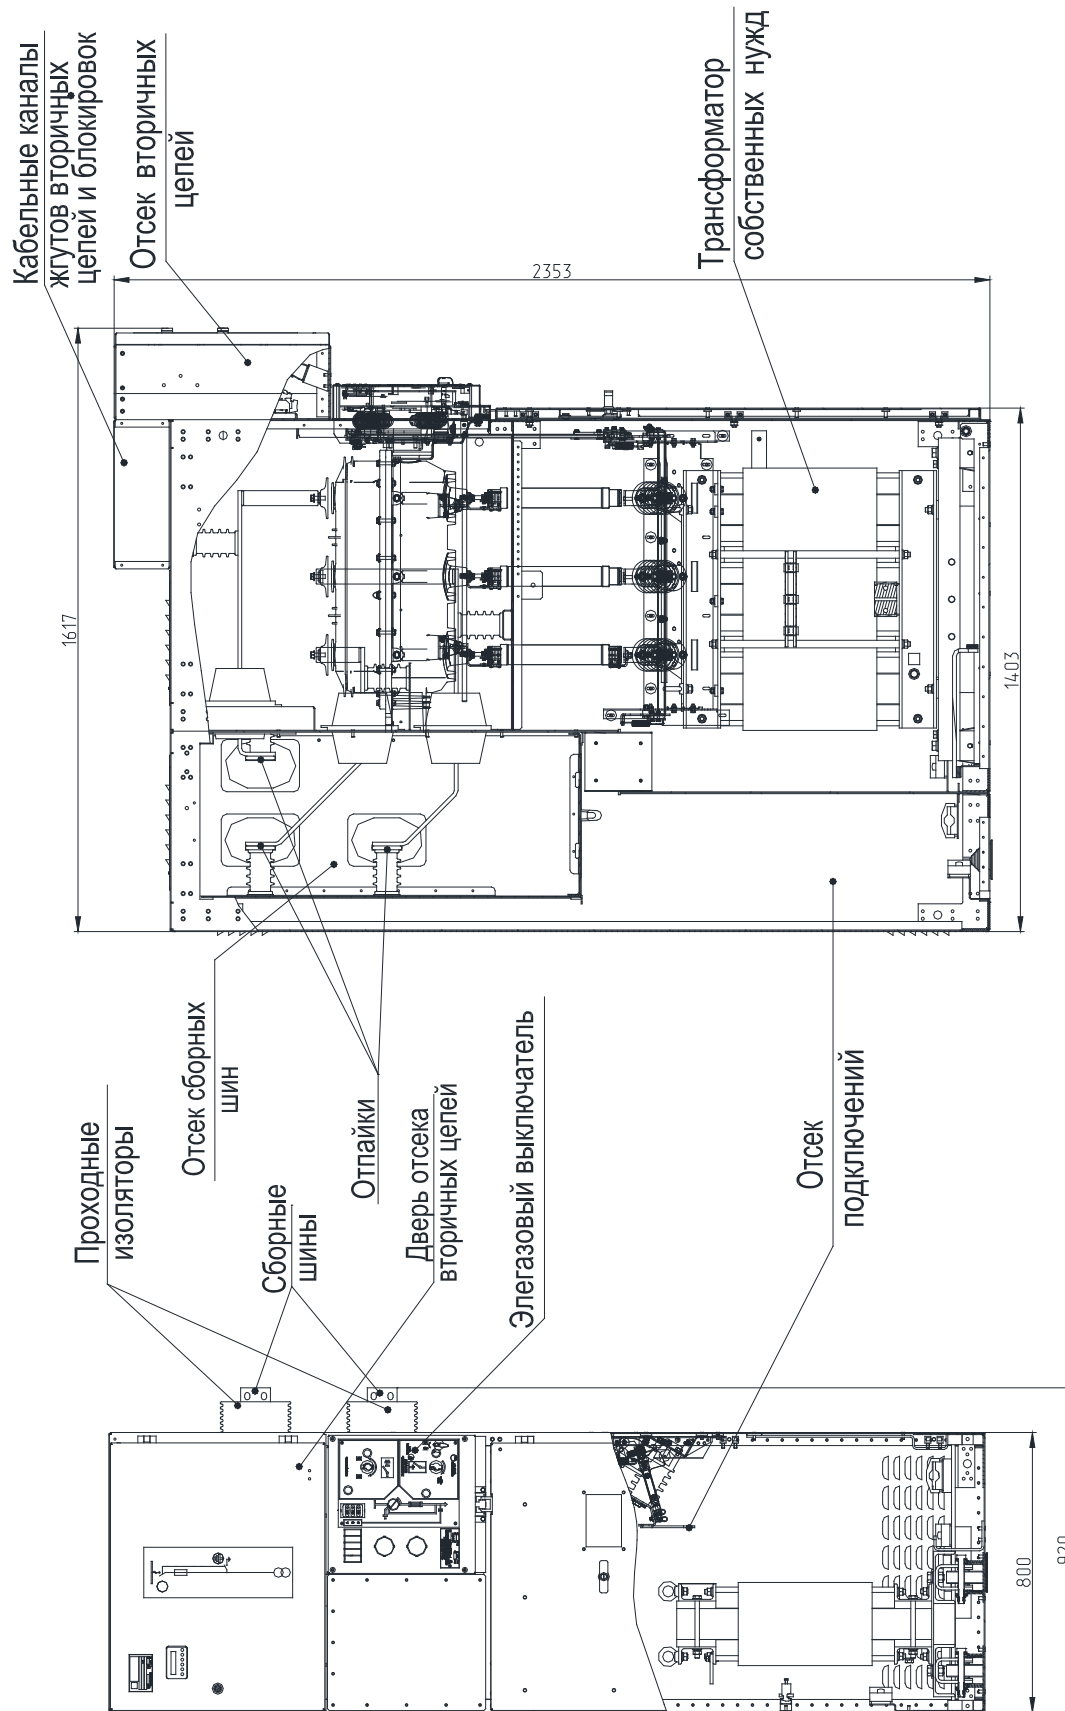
Габаритные размеры и компоновка шкафа КРУ с ТСН до 40 кВА и трехпозиционным элегазовым выключателем нагрузки
